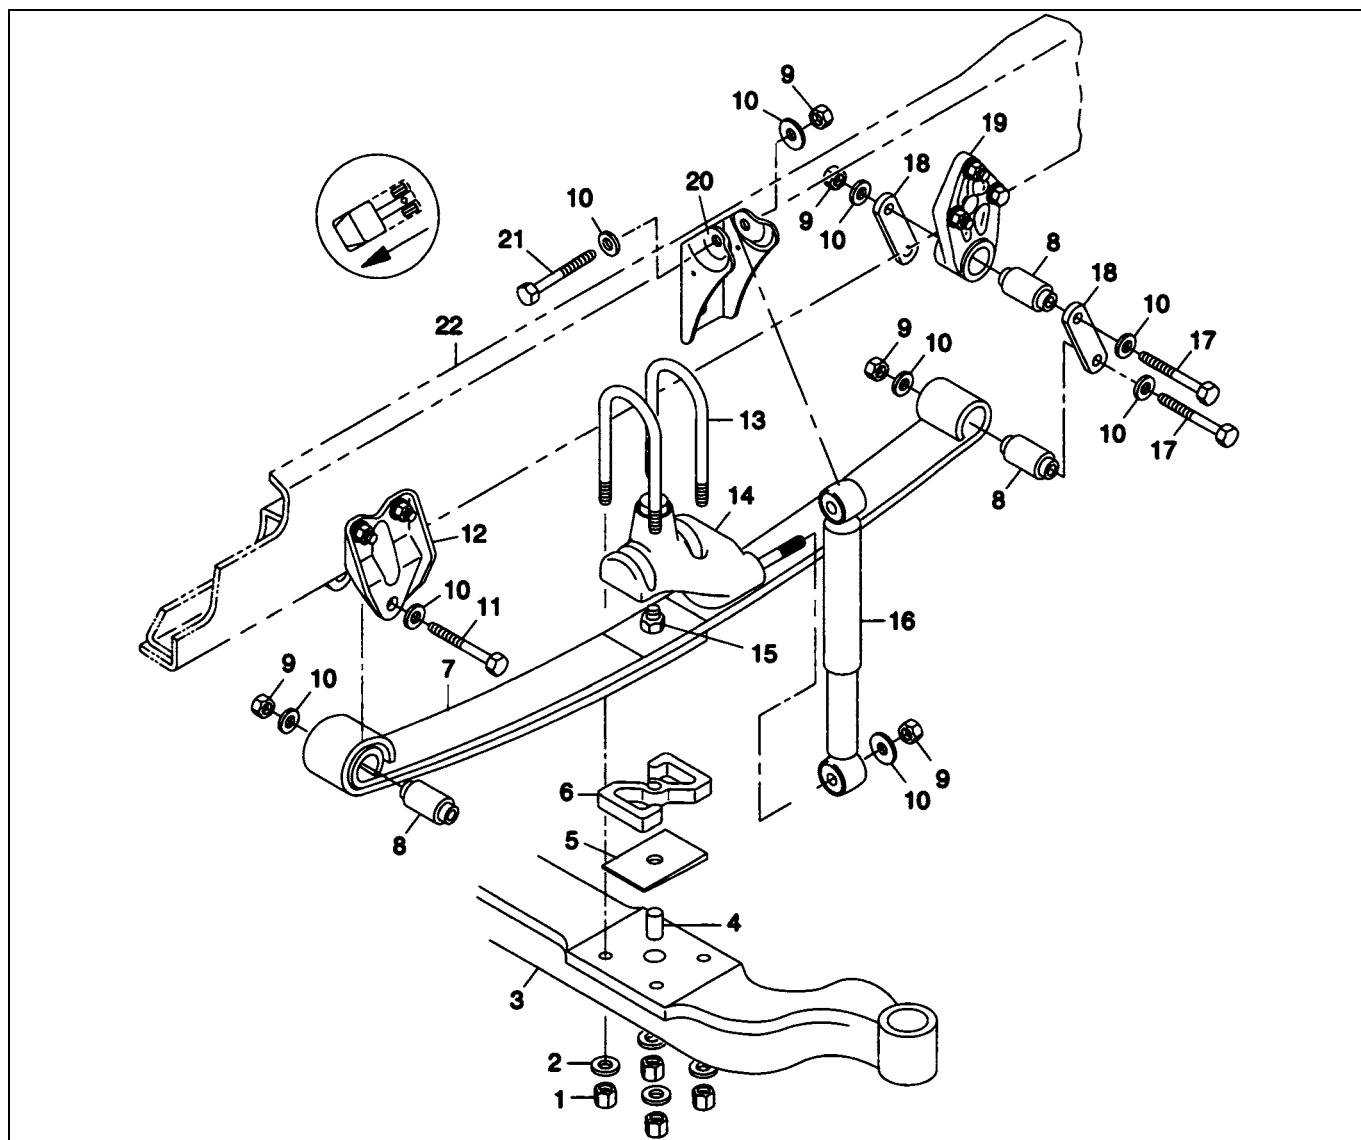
Передняя подвеска с резиновыми втулками. 1 - гайка стремянки рессоры, 2 - шайба, 3 - балка моста, 4 - штифт, 5 - проставка (клин) регулировки продольного наклона шкворня, 6 - прокладка, 7 - рессора в сборе, 8 - резиновая втулка, 9 - контргайка (3/4"-10), 10 - закаленная шайба, 11 - болт ушка рессоры, 12 - передний кронштейн рессоры, 13 - стремянка, 14 - ограничитель хода подвески и нижняя опора амортизатора, 15 - центральный болт рессоры, 16 - амортизатор, 17 - болт серьги (3/4"-10), 18 - серьга рессоры, 19 - кронштейн серьги, 20 - верхняя опора амортизатора, 21 - болт (3/4"-10), 22 - лонжерон рамы.
